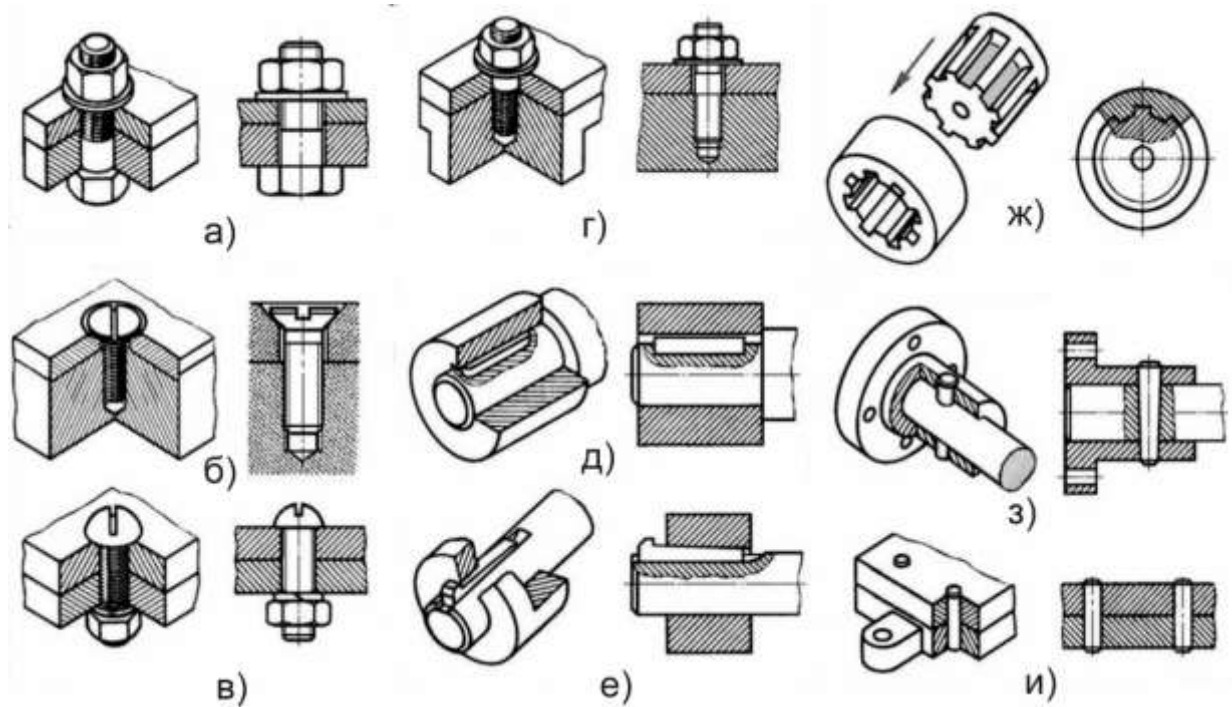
Види складальних роз'ємних з'єднань: а – болтове; б, в - гвинтове; г – шпилькою; д, е - шпонкове; ж – шліцеве; з, и - штифтове.
